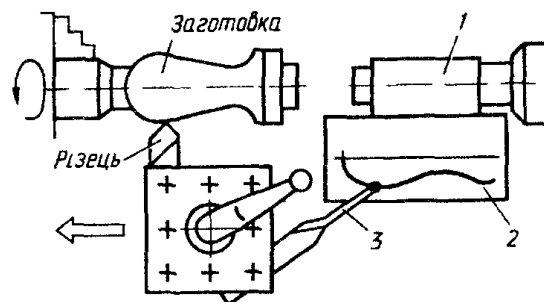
Обробка фасонних поверхонь способом поєднання двох подач із контролем за кресленням: 1 - тримач планшета; 2 - планшет з кресленням фасонного контуру деталі; 3 - рейсмус
